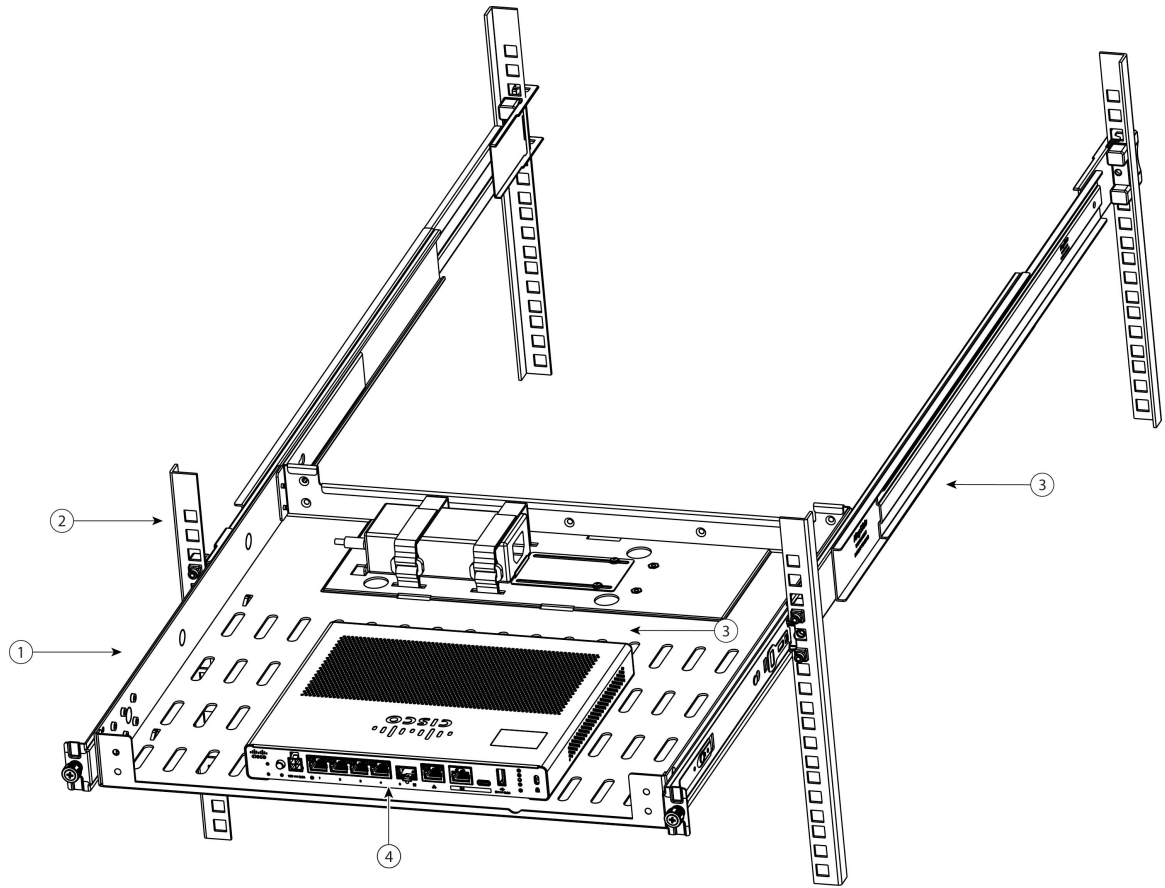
Instale las guías de deslizamiento en el estante de montaje en rack
